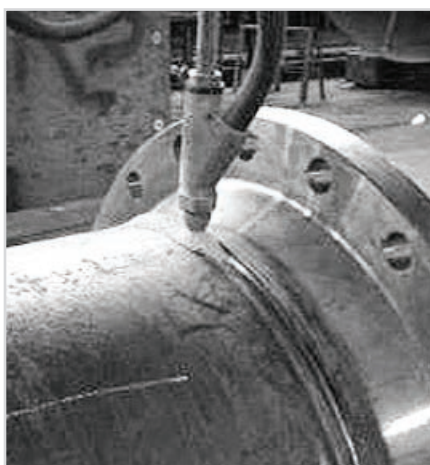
Монтаж приварочного встык фланца приваркой под слоем флюса
